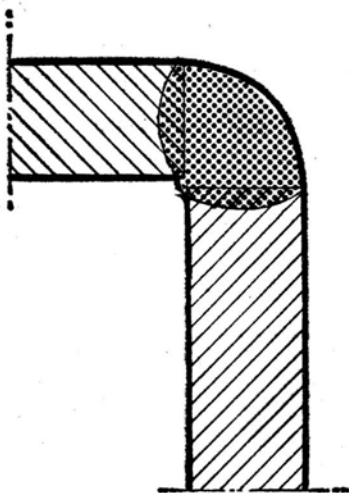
SOLDADURA DE ANGULO, EN ESQUINA
